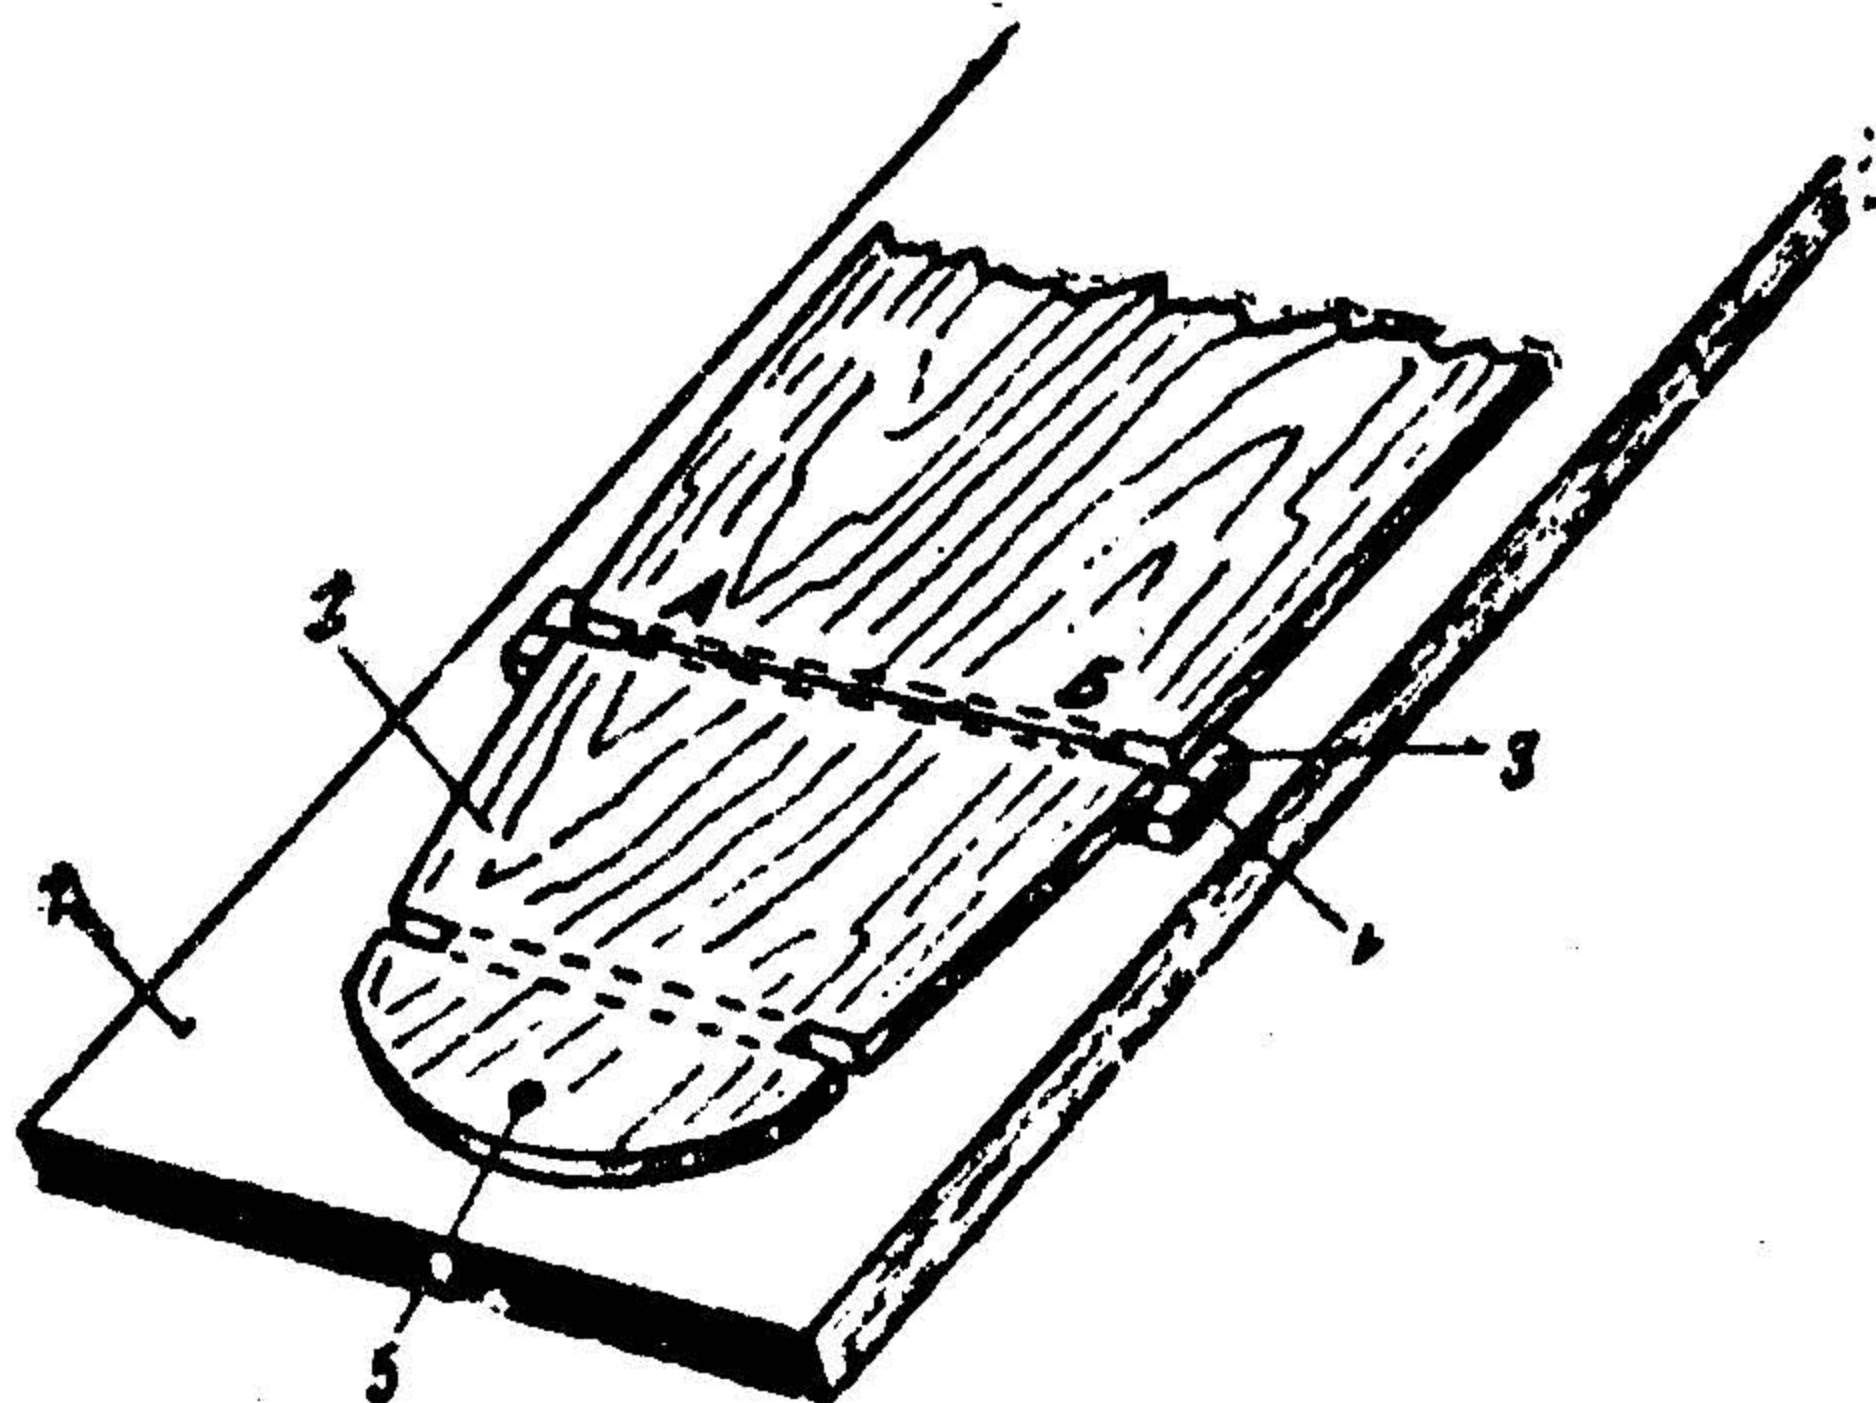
Проверка крепления настила палубы: 1 — стапельная доска; 2 — палубный настил; 3 — стапельный брусок; 4 — проверочная линия; 5 — гвоздь
